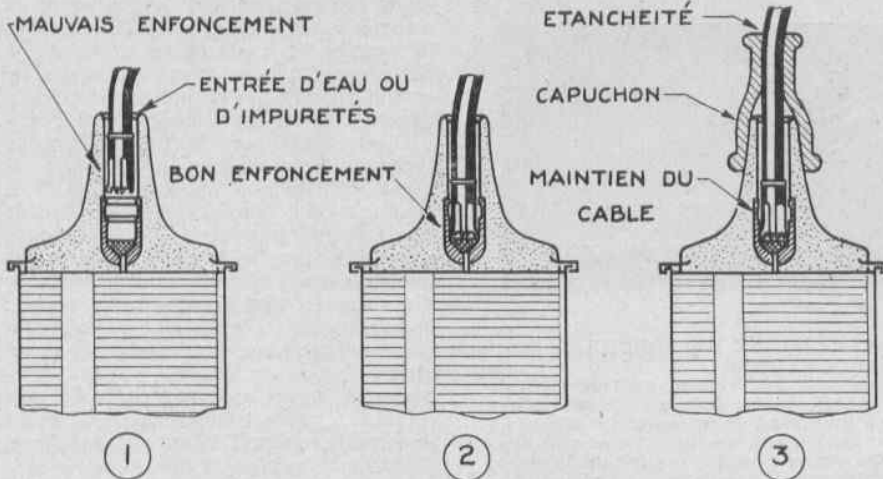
LE MONTAGE CORRECT DU CÂBLE DE PRISE HAUTE TENSION SUR LA BOBINE.
